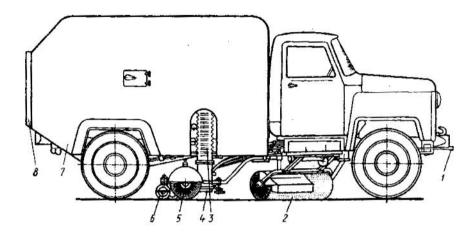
Вакуумно-уборочная машина: 1 – разбрызгивающая форсунка; 2 – цилиндрическая щетка; 3 – всасывающий рукав; 4 – заборное сопло; 5 – лотковая щетка; 6 – опорное устройство; 7 – кузов; 8 – задняя крышка
